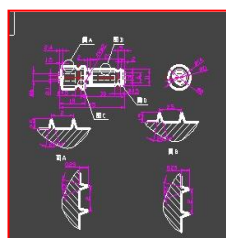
腰骶椎带锁轴向内固定器中轴植骨融合器 CAD 构件图
